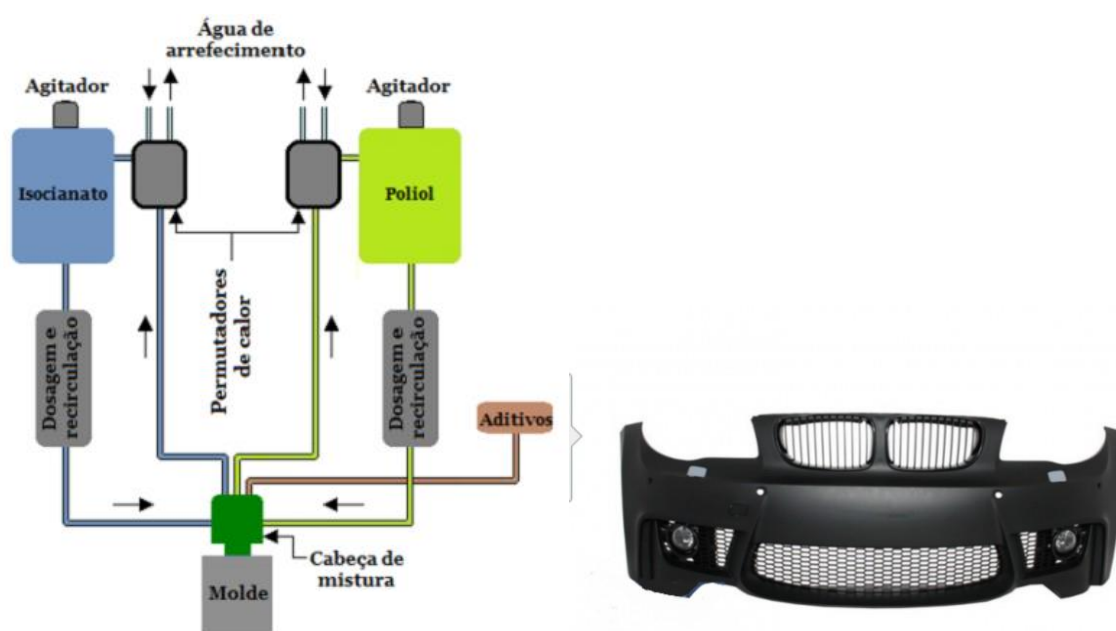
Processo de moldagem RIM, à direita, o parachoque de um carro, fabricado utilizando o RIM como processo de manufatura.
